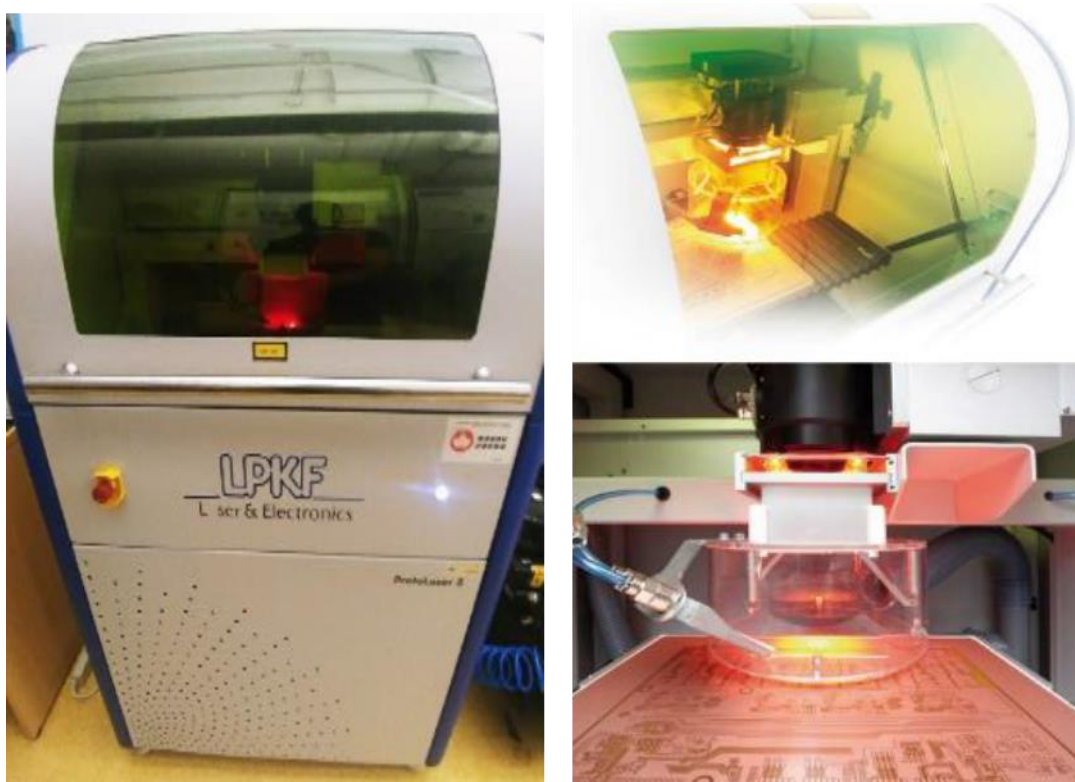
Machine de fabrication laser LPKF ProtoLaser S de l'INRS [67].
